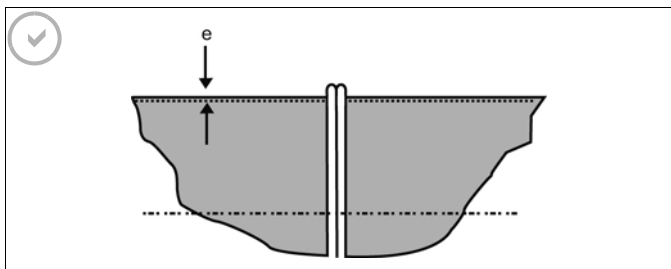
Сварка встык с равными наплавленными валиками (успешно)
